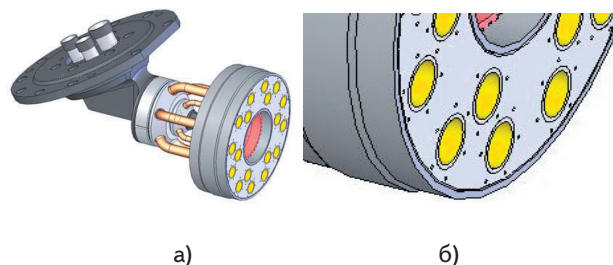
Общий вид (а) прямоточной трубчатой горелки и фрагмент (б) ее фронтальной части
